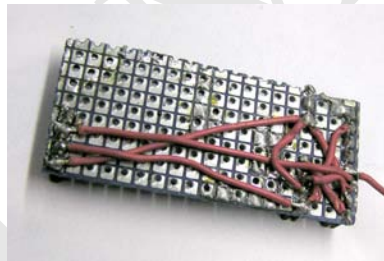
Soldaduras en una placa pretaladrada
